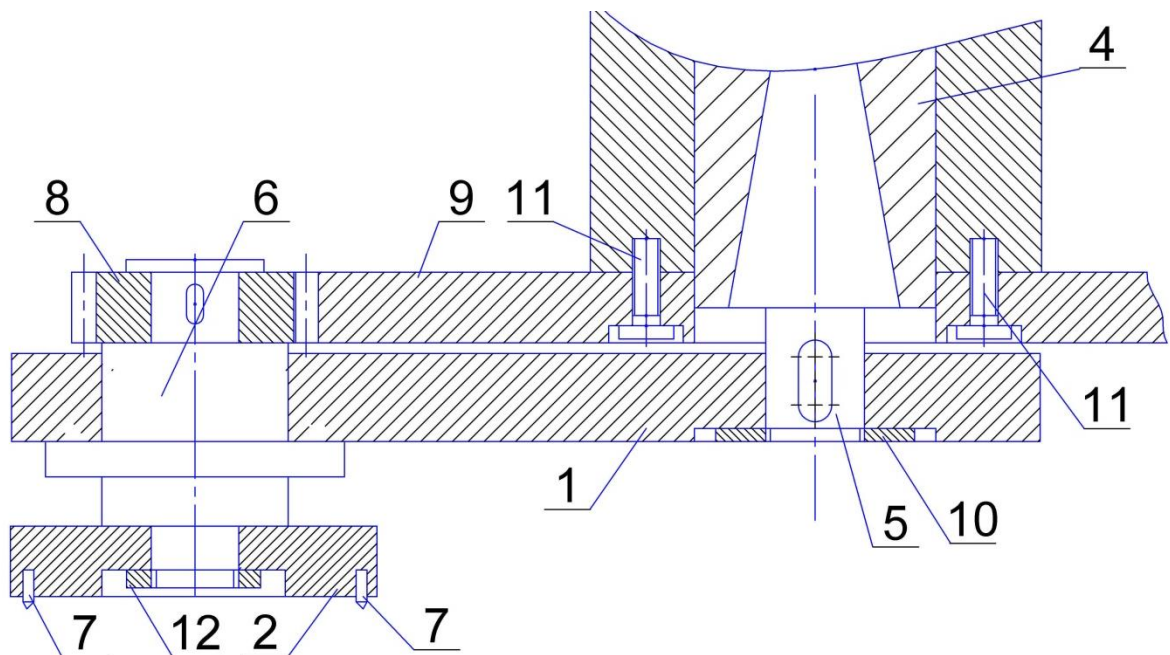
Загальний вигляд фрезерної головки з однією торцевою фрезою
